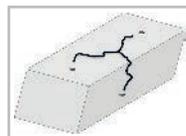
Рекомендуемая последовательность нанесения швов в процессе сварки — наплавки при восстановлении протяженных участков детали
